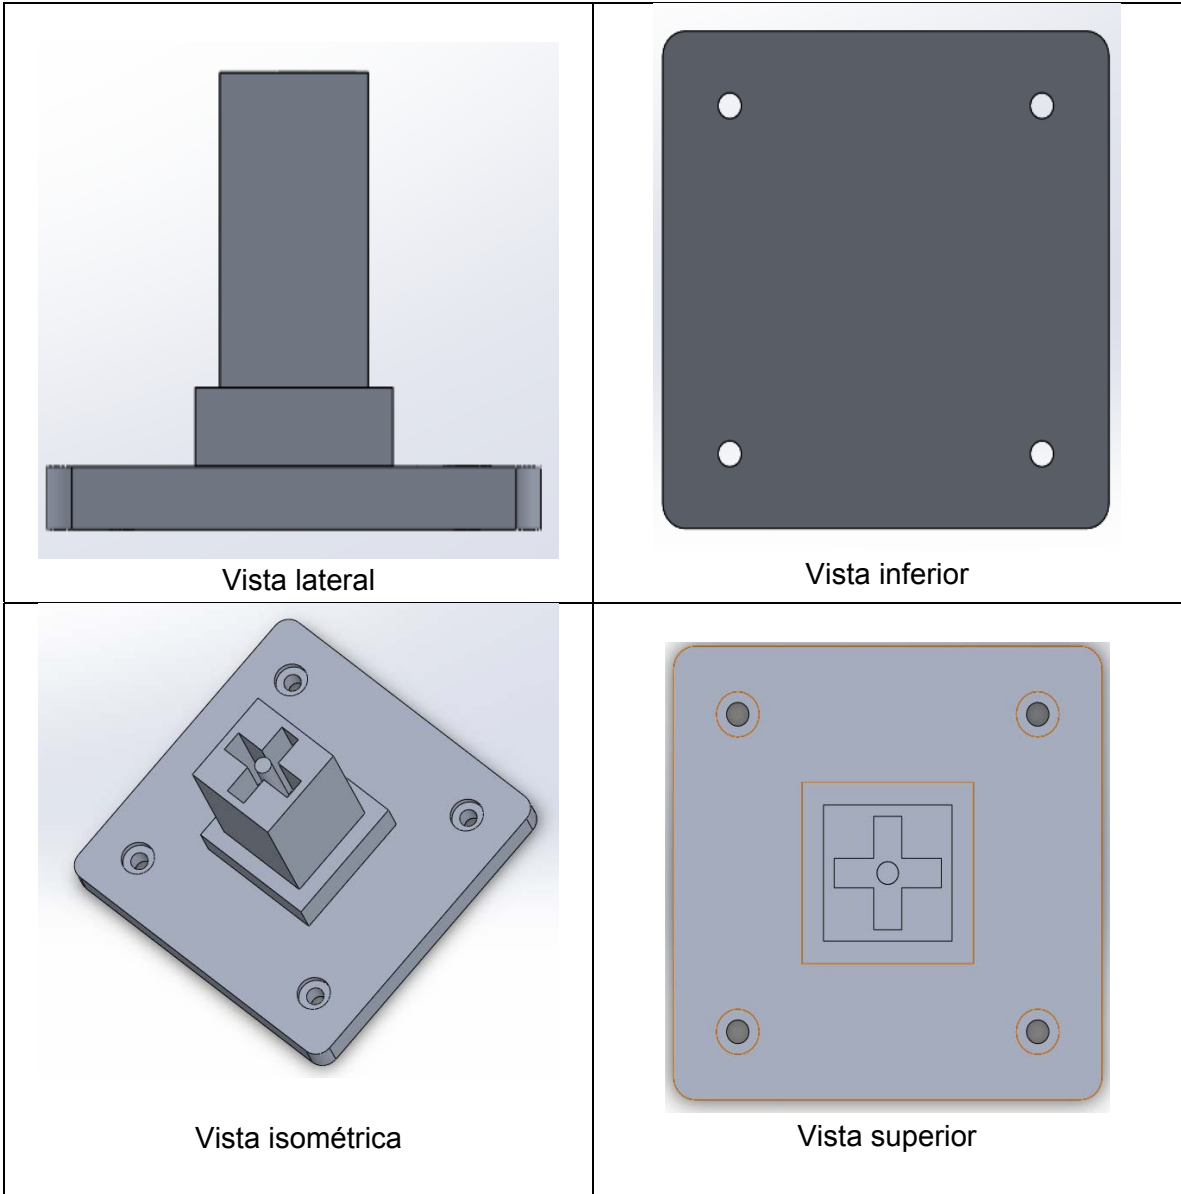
Vistas del diseño en Solidworks de la base de brazo mecánico
